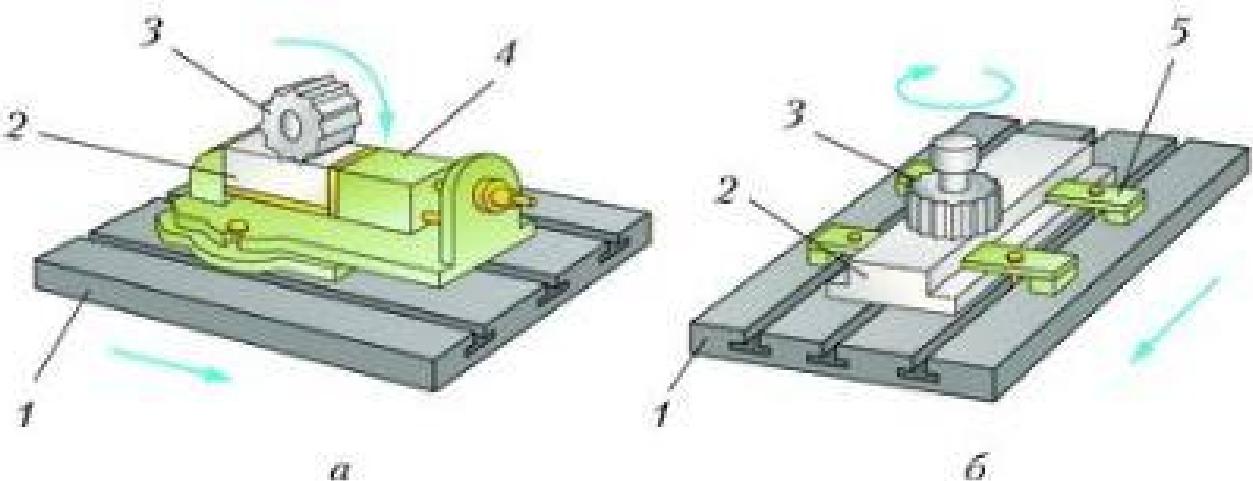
Фрезерование плоскостей: *а* – цилиндрической фрезой в тисках;
